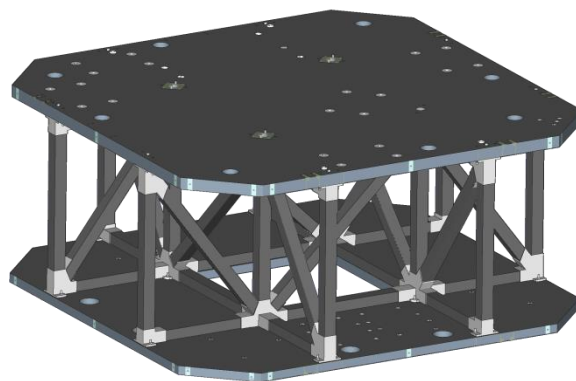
Общий вид корпуса аппаратного блока платформы КА "Січ-2М"
